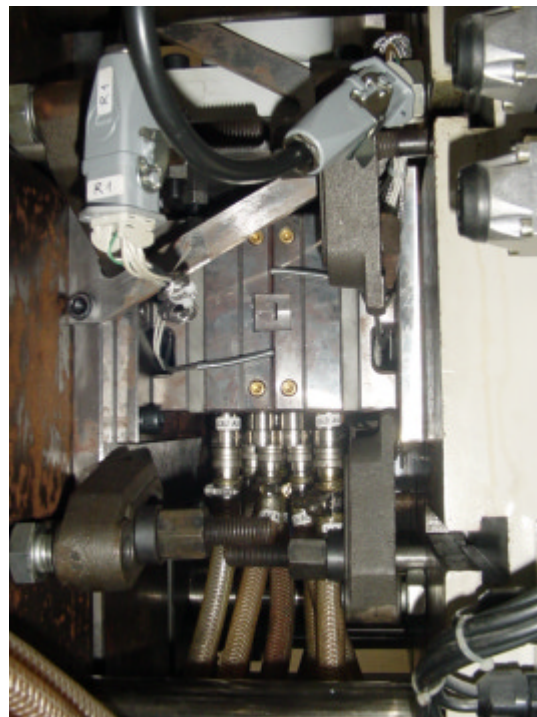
Vista do molde montado do lado oposto ao operador
